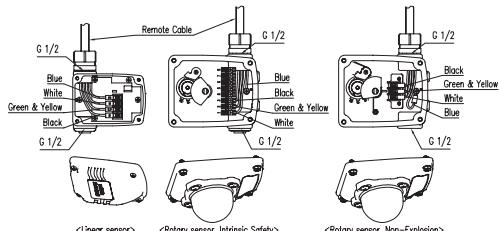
Sensor remoto y cables del modelo YT-2501L
